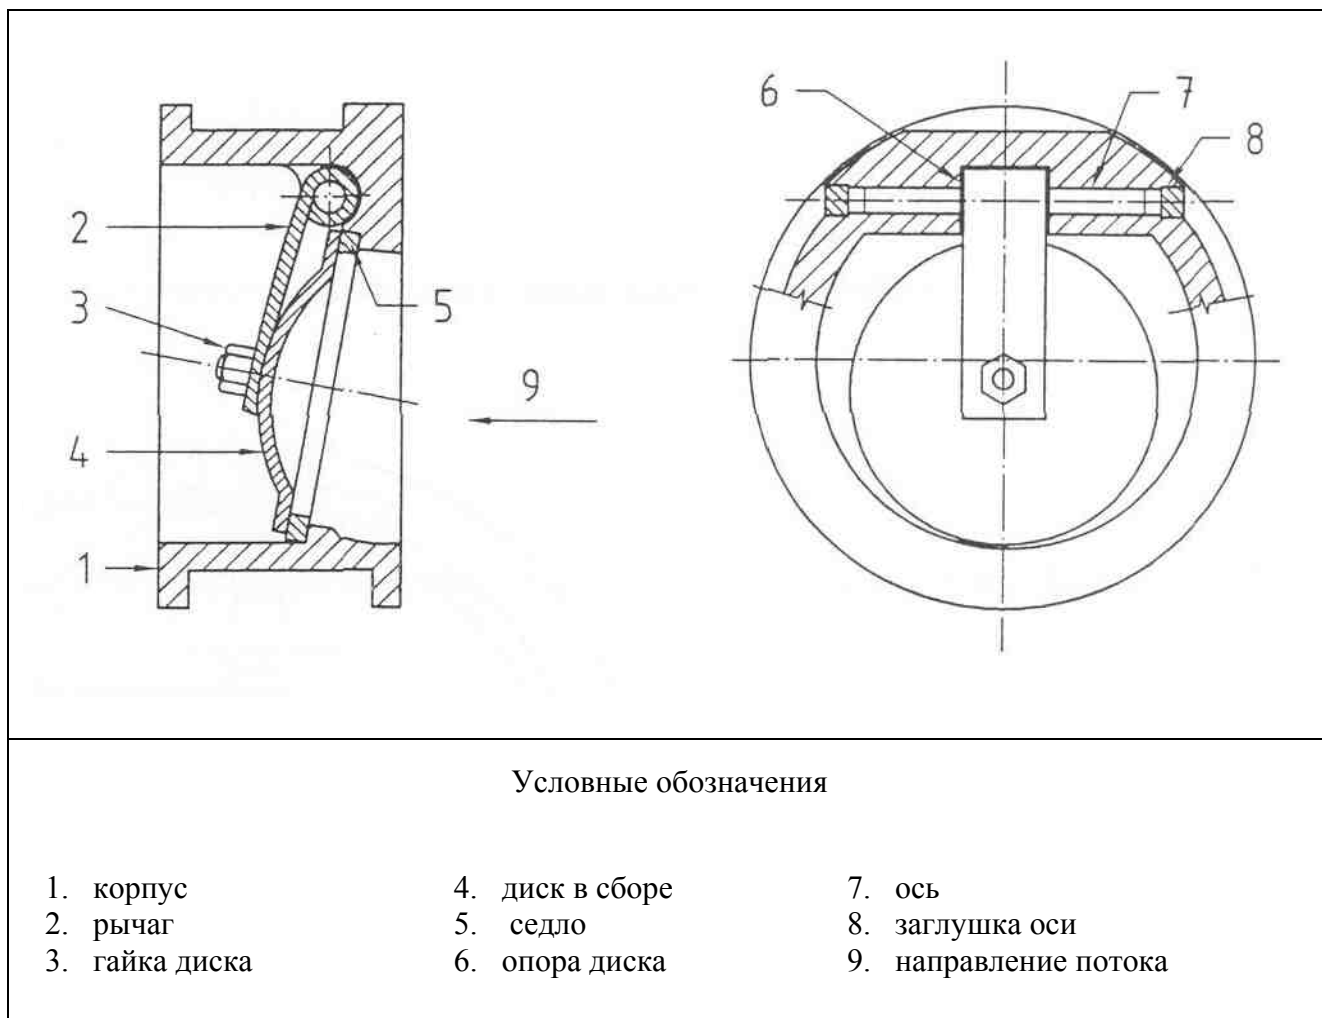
Однодисковый обратный затвор с полноразмерным корпусом
